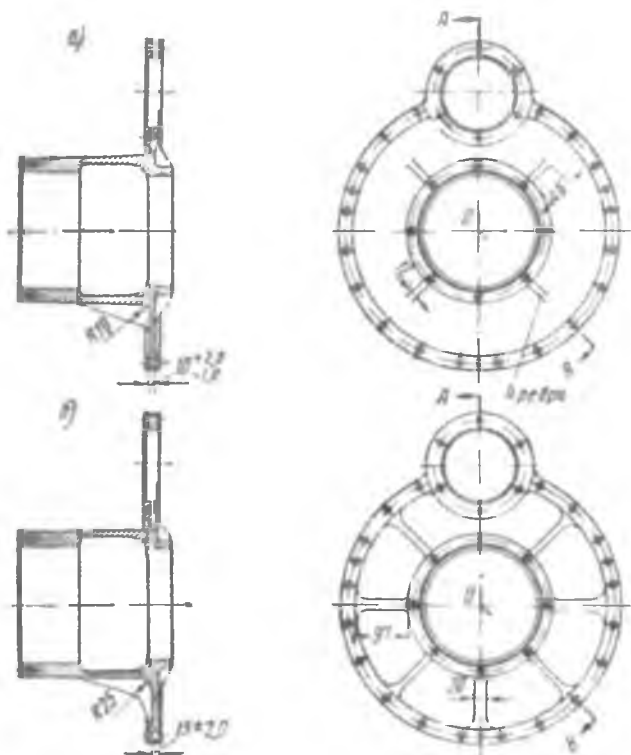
Крышка бортового редуктора: а — до усиления, б — после усиления
